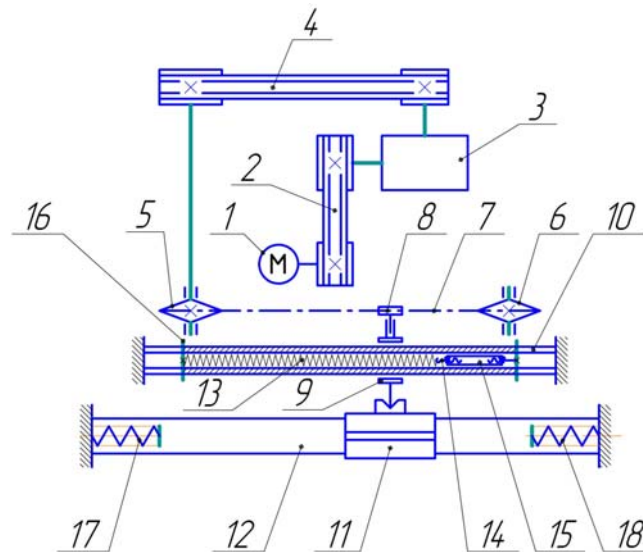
Кінематична схема приводу рукавичного автомата з ПЗДН, що містить дві пружини стиску
